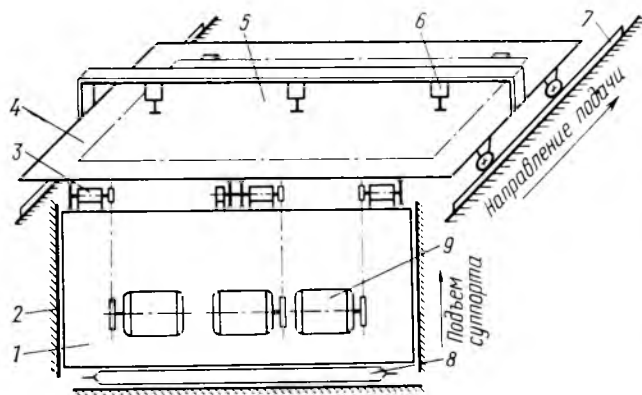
Схема станка для выборки поперечных пазов под раскладку
